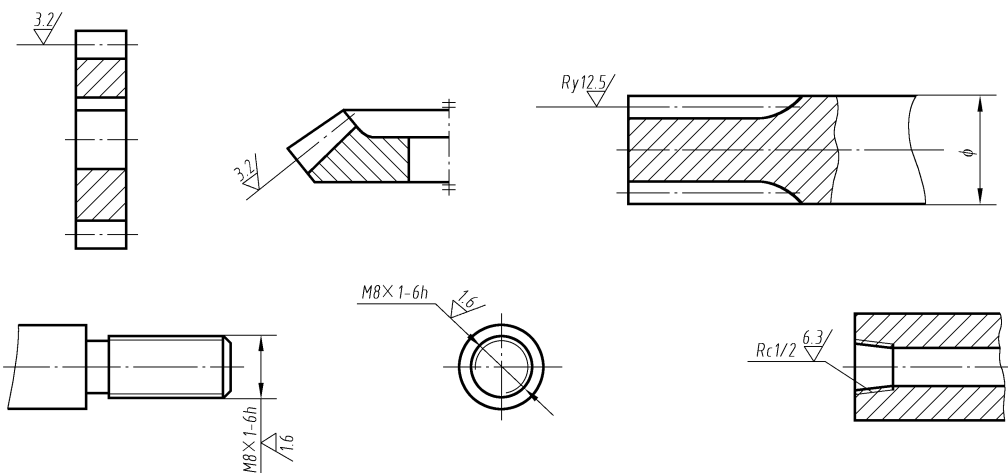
齿轮、花键、螺纹表面粗糙度代号的标注
